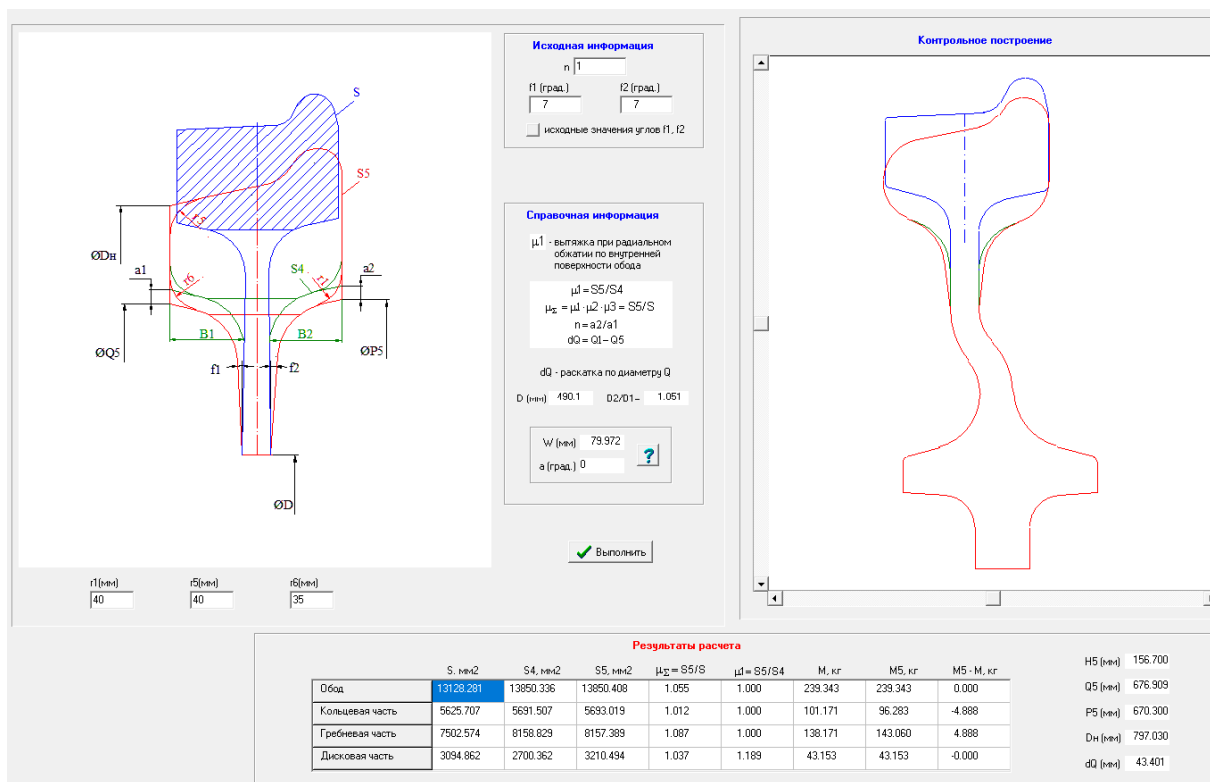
Уточненный расчет основных параметров обода с гребнем колесной заготовки и проектирование калибровки для формовочного прессы
